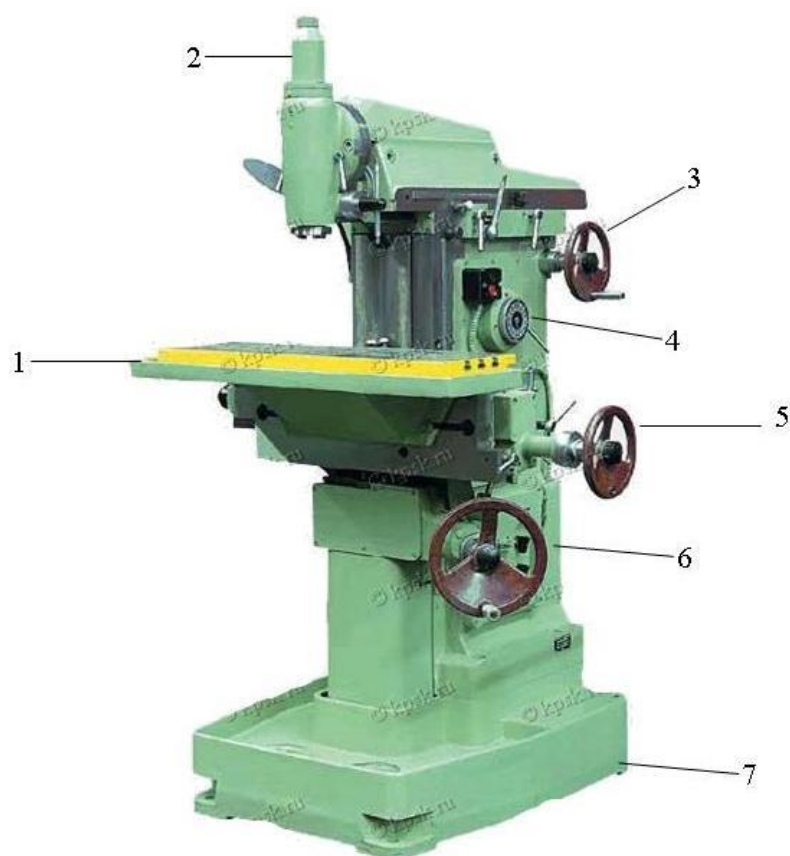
Общий вид универсального фрезерного станка СФ 676
